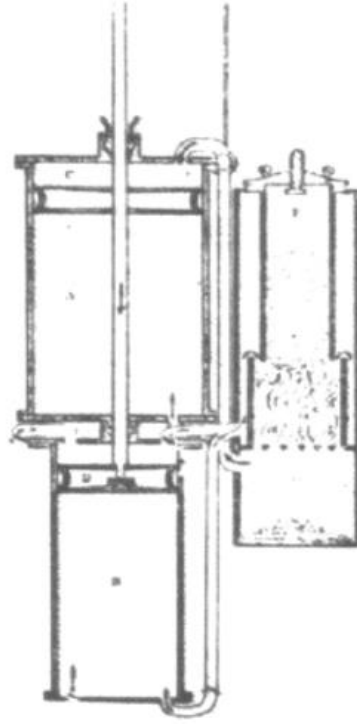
Huygens'in tasarladığı barut motoru [3].
